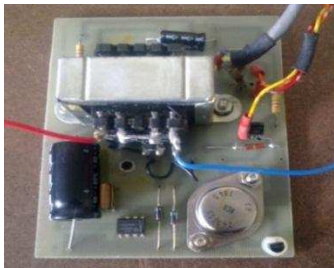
21 Estado Inicial de la Máquina de Ensayos Universales - Circuito Control de Posición
